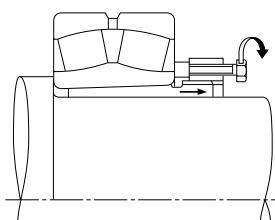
Extracción del Manguito de Desmontaje Utilizando una Tuerca de Desmontaje (2)
